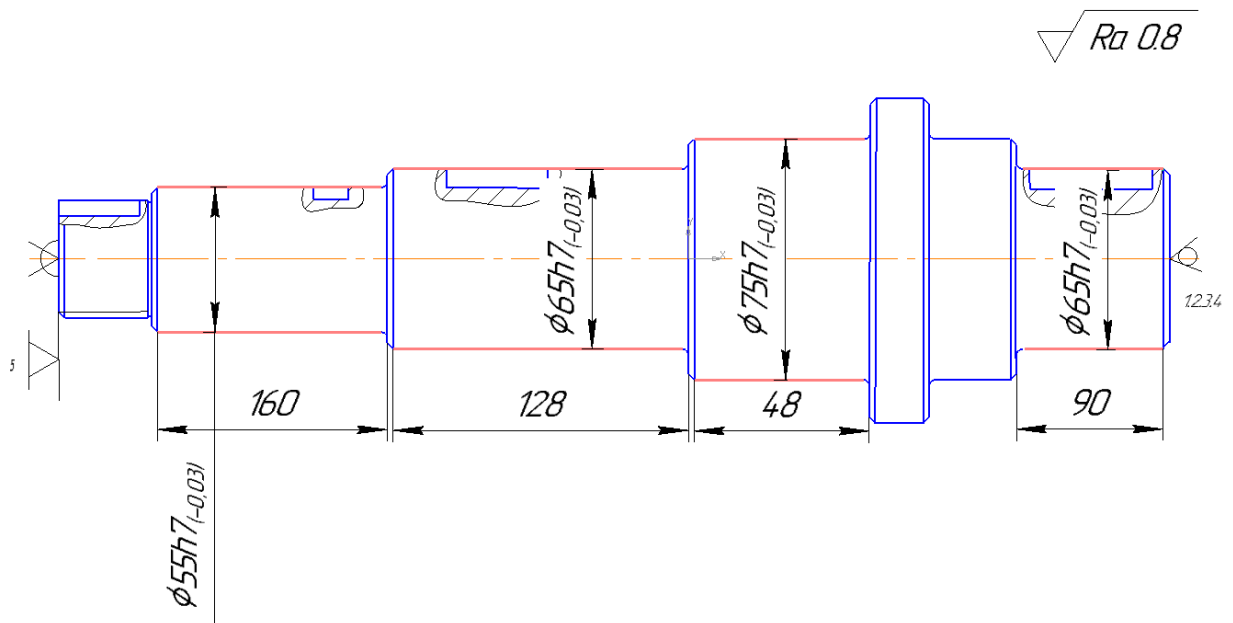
Операційний ескіз (операція 070)
